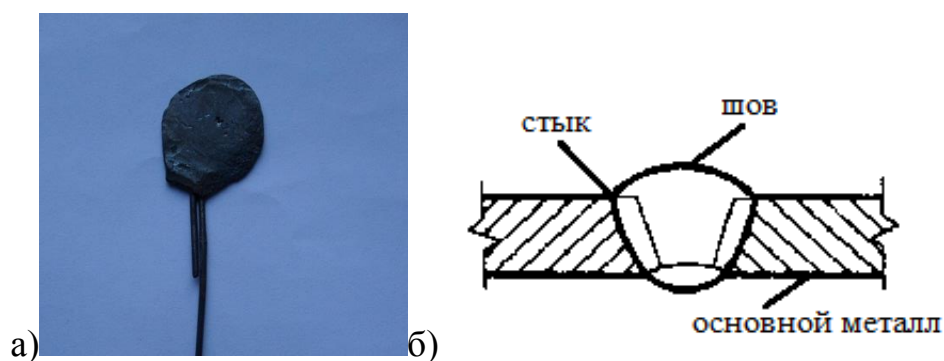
Образцы для определения химсостава сварочной проволоки (а) и сварного соединения (б)
